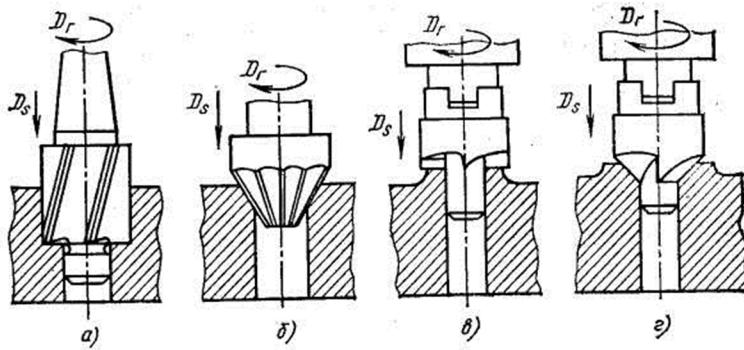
Схема обработки углублений и бобышек зенкерами и цековками
